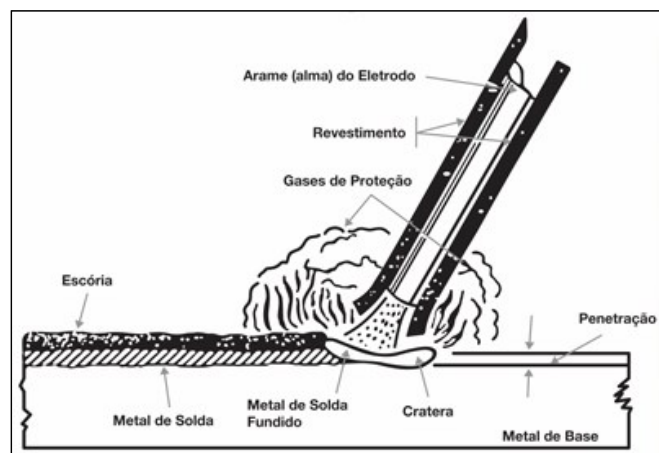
Processo de Soldagem Eletrodo Revestido Fonte: ESAB
